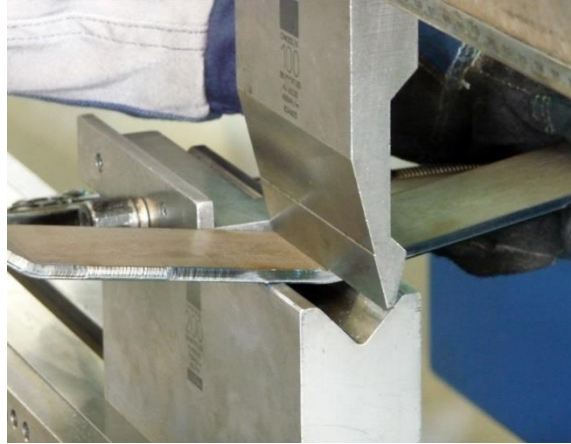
Plegado de piezas metálicas (Fuente: Lasertek)
